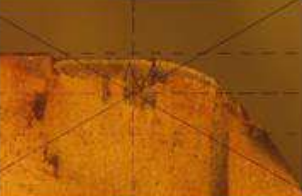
Пластина из быстрорежущей стали P12M3K5Ф2-М (точение жаропрочного сплава; режущий инструмент – P12M3K5Ф2- МП)
